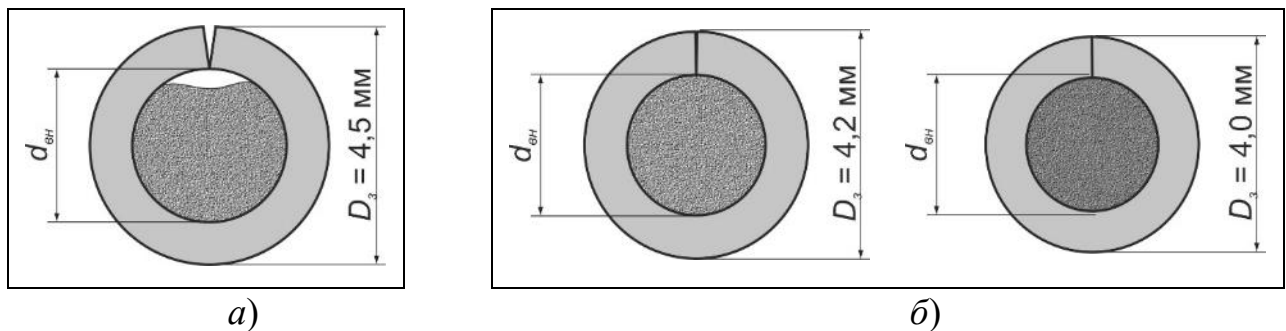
Традиційна формовка заготовки порошкового дроту із стрічки товщиною 0,8 мм на виході з формувального агрегату (а) та запропоноване доформування заготовки порошкового дроту двома додатковими блоками роликового редукування (б).
